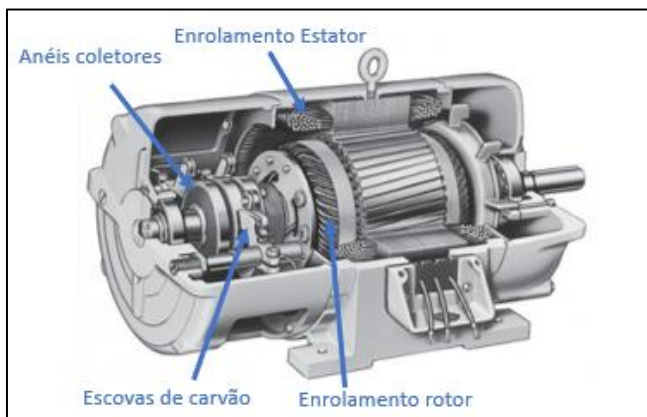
Motor de rotor bobinado. Adaptado de [14].
